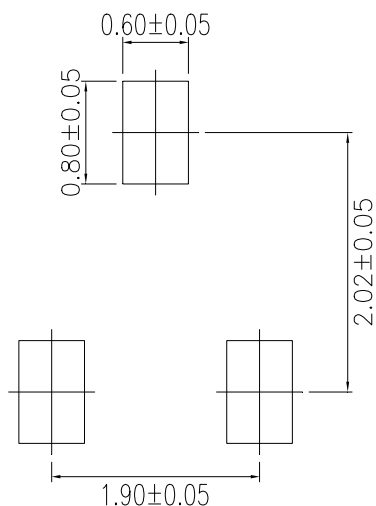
SOT23-3L 封装形式 PCB 焊盘推荐(unit: mm)..
